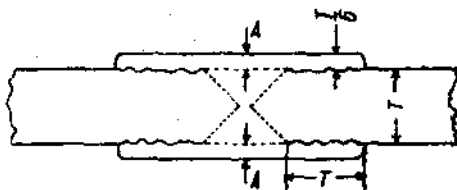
Сварка железными электродами без применения шпилек.
